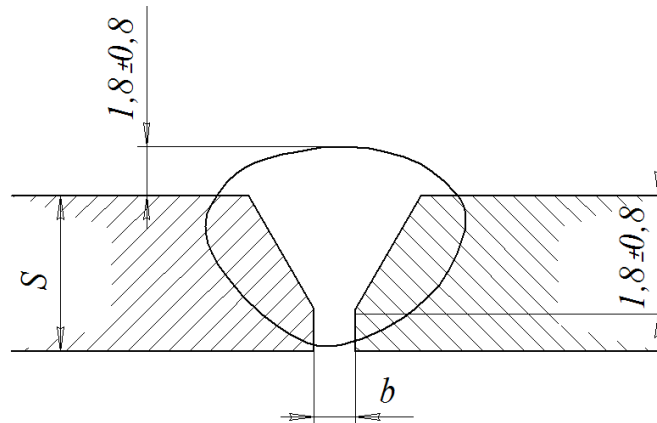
Геометрические размеры сварного стыка
